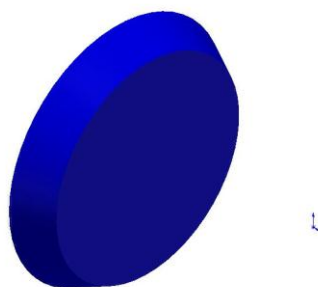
Peça da Matriz para Construção da Boca de Enchimento
